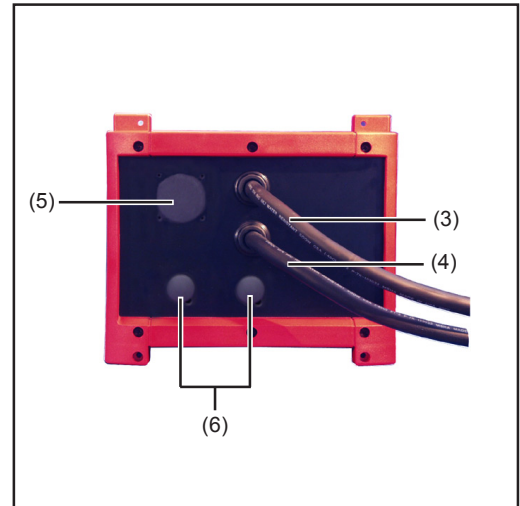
Face arrière transformateur automatique MW 2600 575 V
